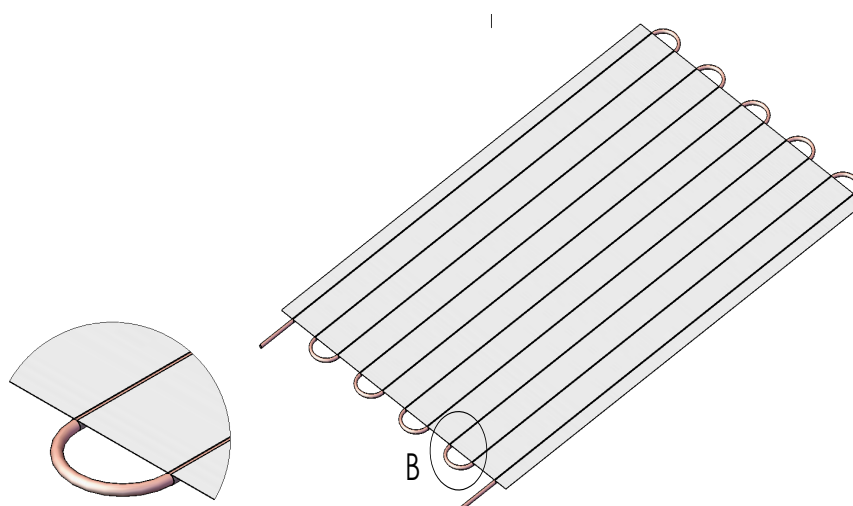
Desenho do evaporador estático com a serpentina e a placa (aleta) dissipadora de calor
